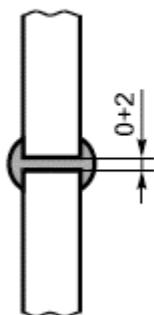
Рекомендуемые виды вертикальных сварных соединений стенки
